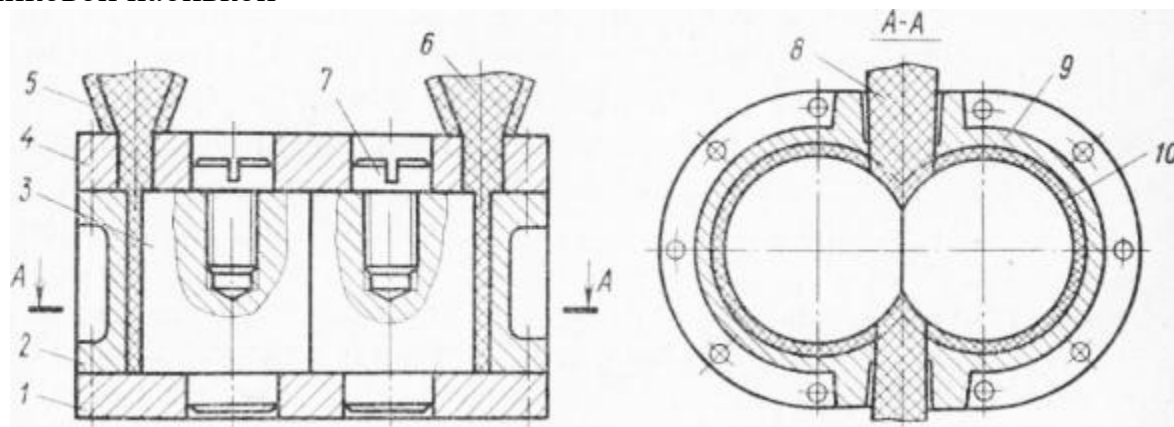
Схема к ремонту шестеренчатых насосов пластмассовыми композициями
